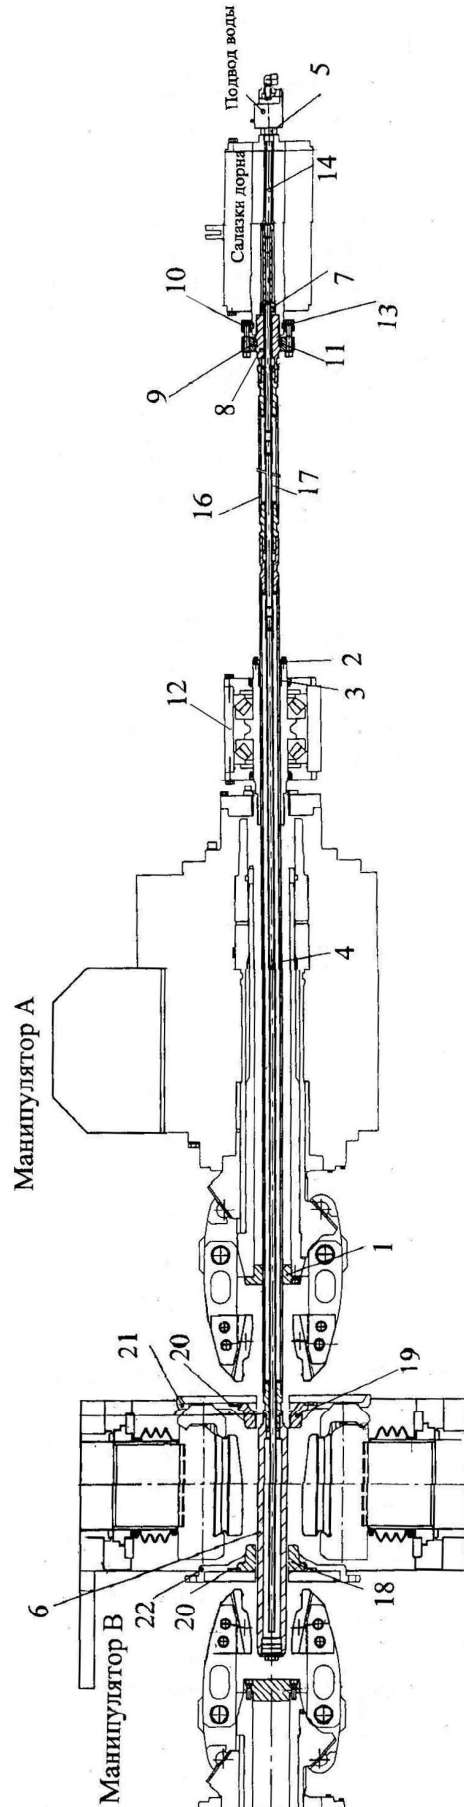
Схема установки инструмента и приспособлений для горячейковки труб
